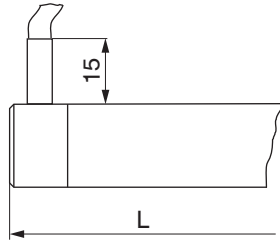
Wegsensor Typ - CR mit integriertem Kabel (radial)
